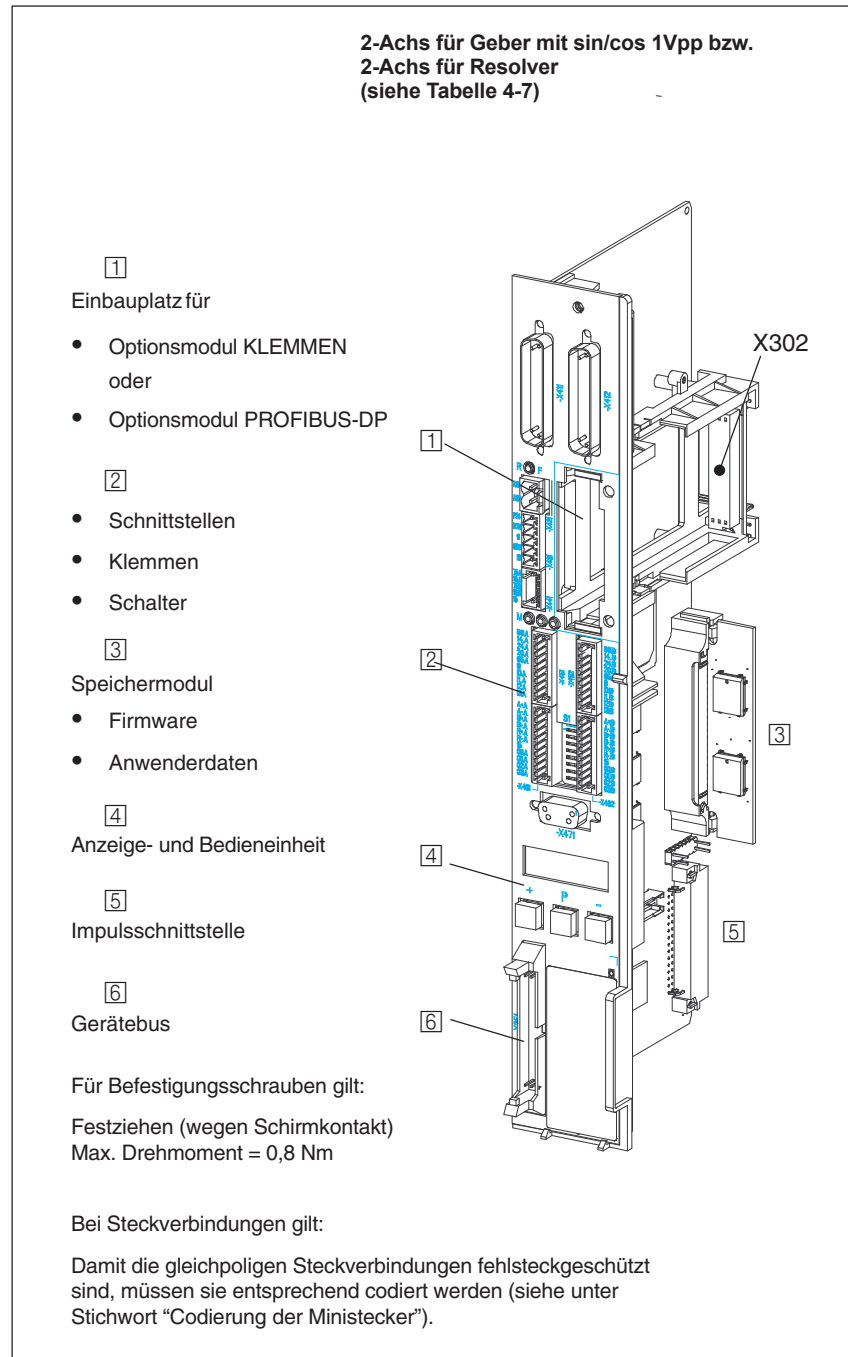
Regelungsbaugruppen für 2 Achsen (SIMODRIVE 611 universal HRS)
